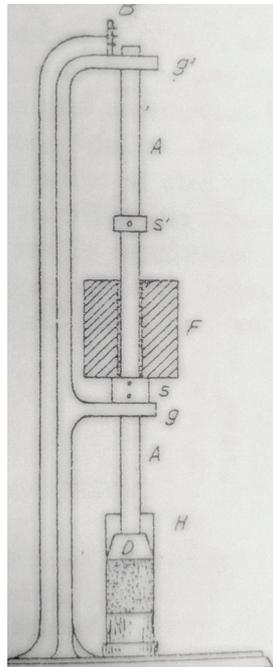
Equipo para ensayo mecánico de arenas de moldeo.
